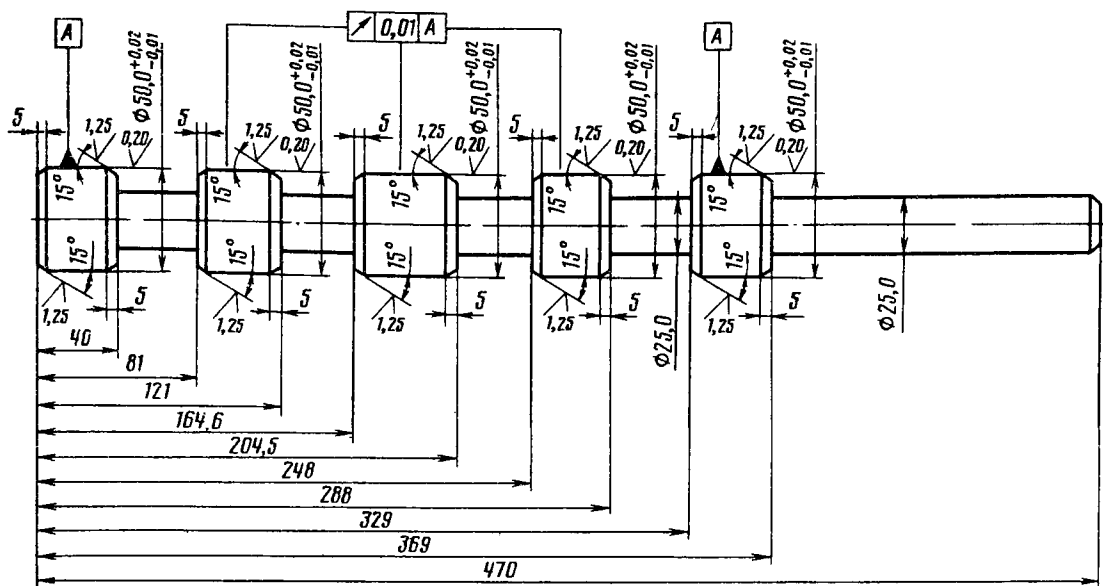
Оправка для проверки соосности коренных подшипников коленчатого вала
